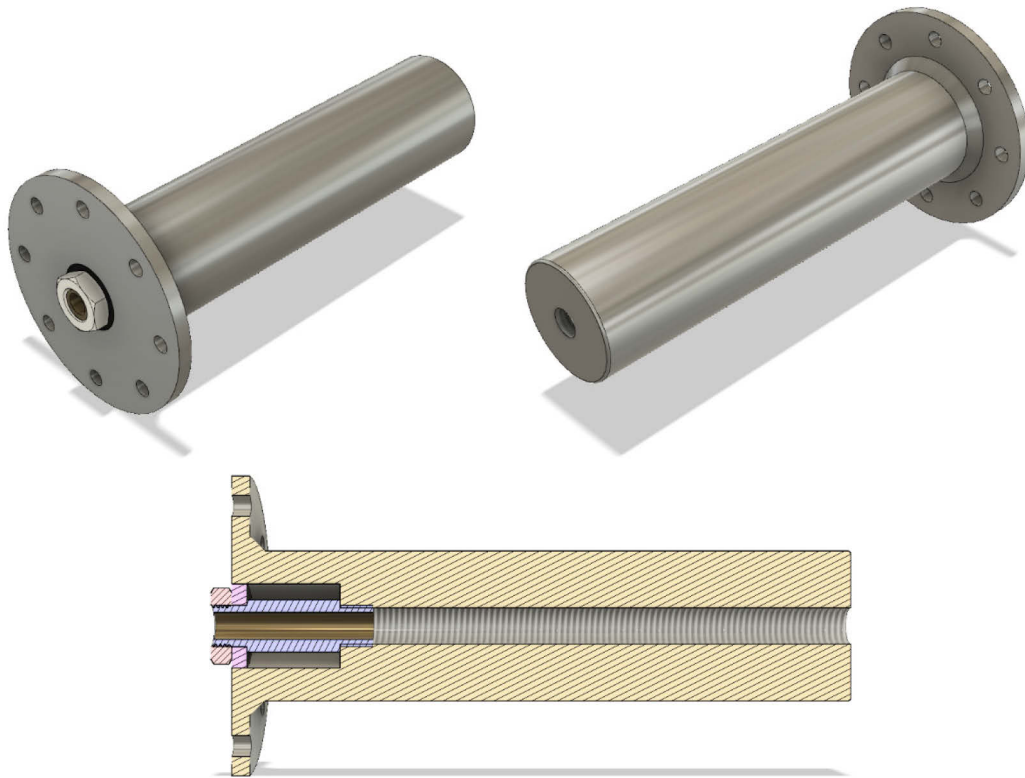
Aktuelle Flanschswelle mit dem Unterdruckventil
